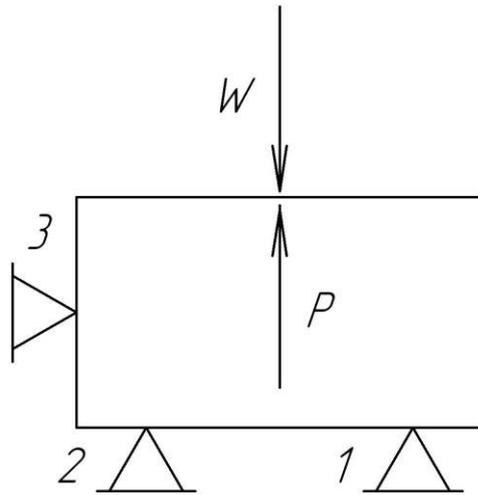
Схема установки, при которой силы резания стремятся оторвать заготовку от опор
